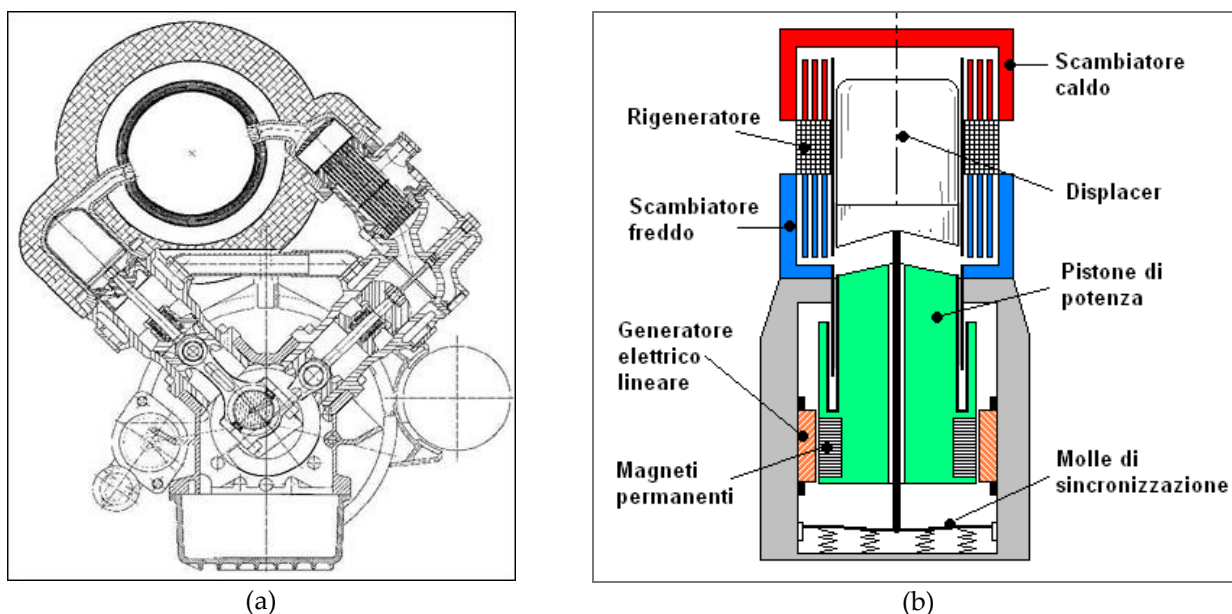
Motori Stirling (a) a guida cinematica e (b) a pistoni liberi
